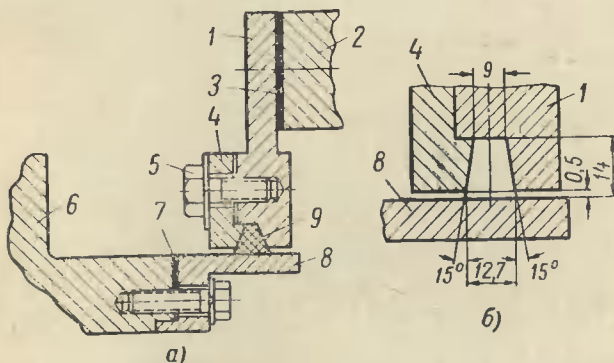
Сальниковое уплотнение, устанавливаемое между корпусом уплотнения и корпусом опорного подшипника.
